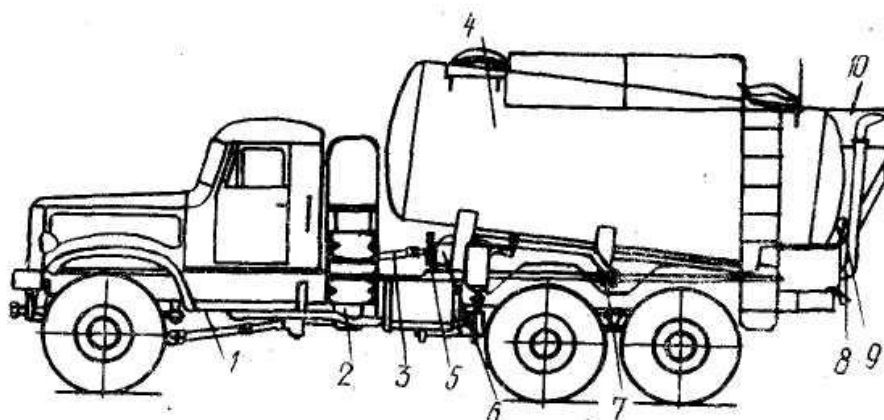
Змішувальний агрегат ЗАЗ-30
